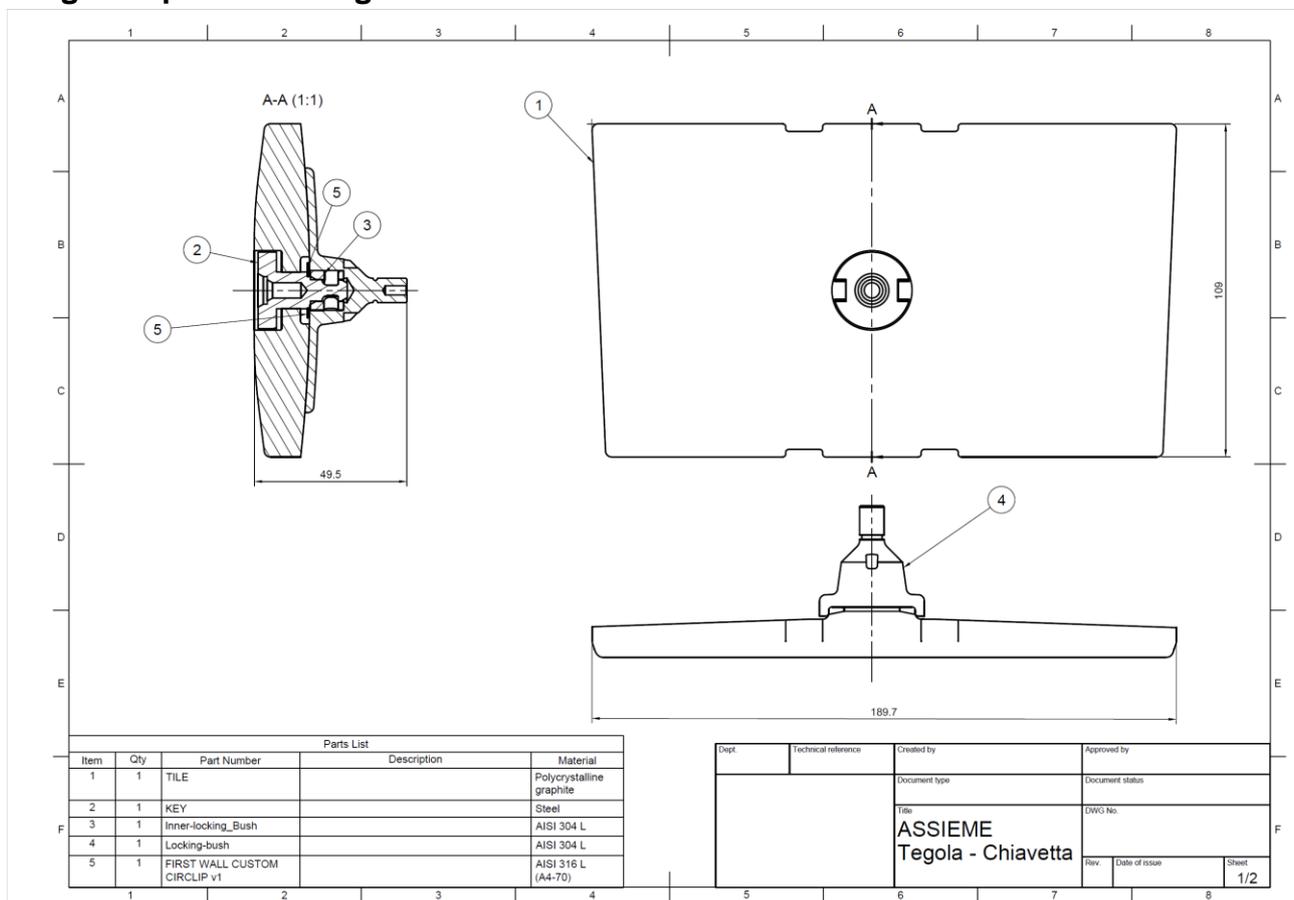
disegno di assieme "tegola-chiavetta-locking bush"
